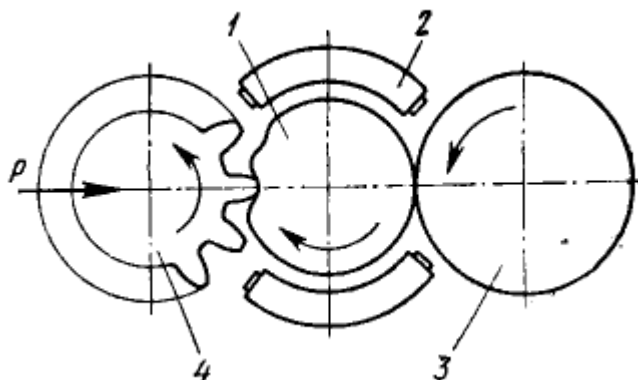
Схема горячей накатки зубьев зубчатого колеса:
